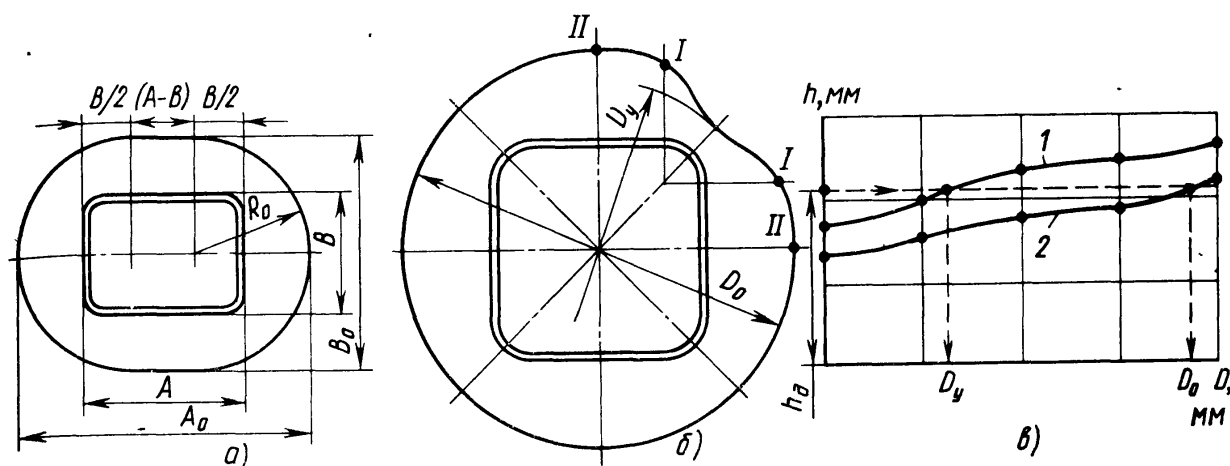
Заготовки для прямоугольных (а), квадратных (б) высоких коробчатых деталей и зависимость высоты детали от диаметра заготовки (в)
